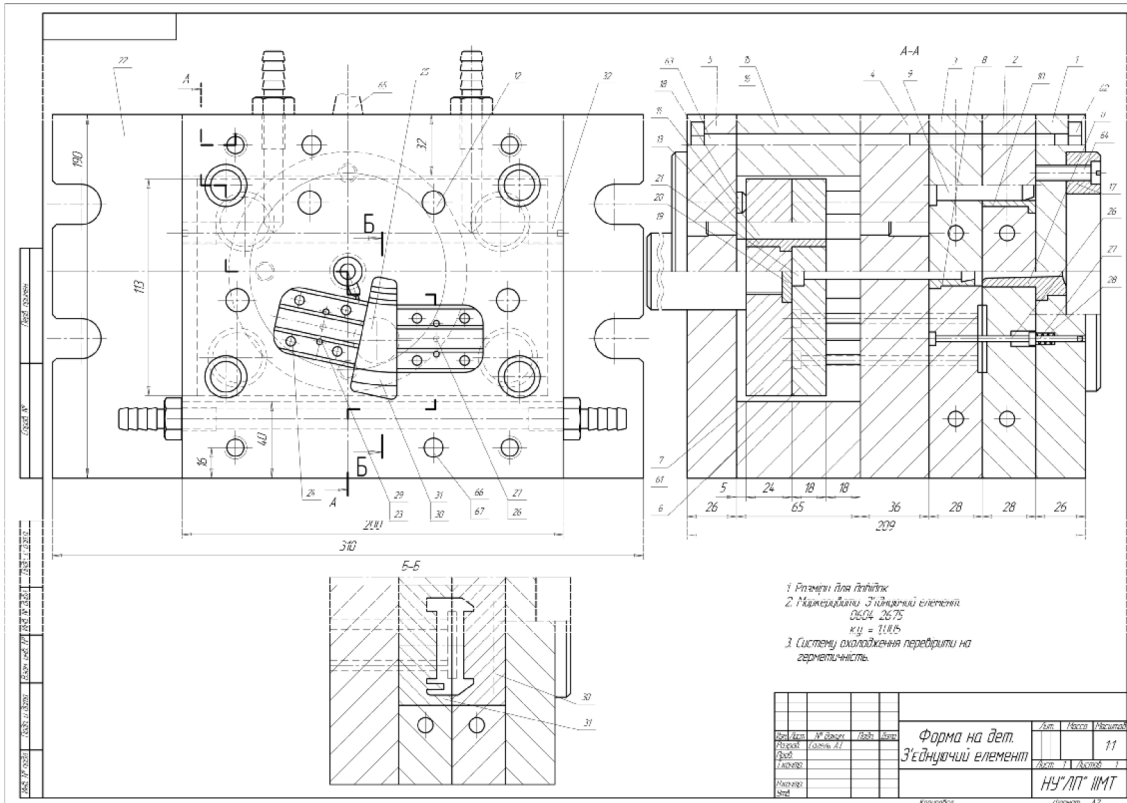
Кресленик пресформи для виготовлення кронштейну
